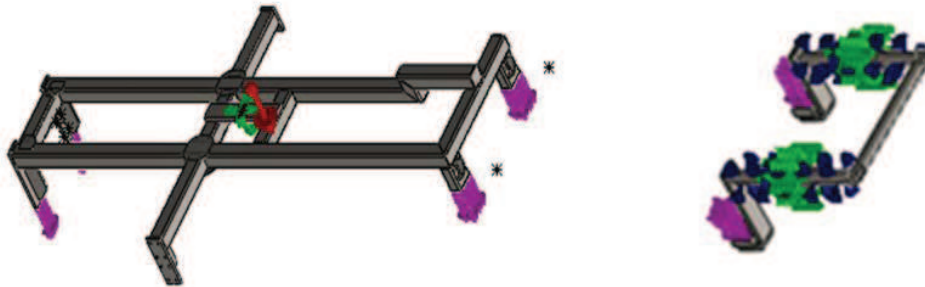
13 Cargas y Restricciones en el Dispositivo de Elevación del Piso Delantero
